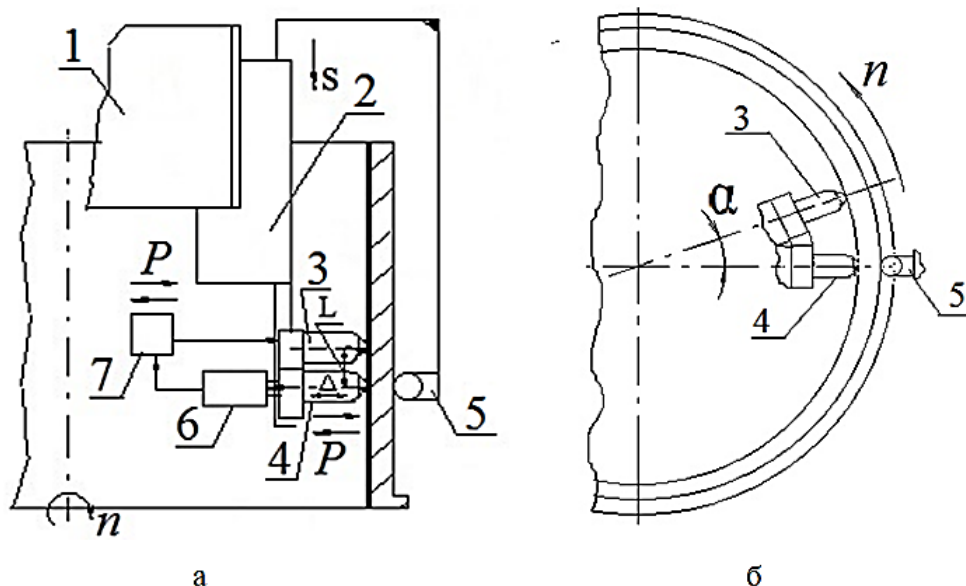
Схема розташування інструмента відносно заготовки під час обробки
